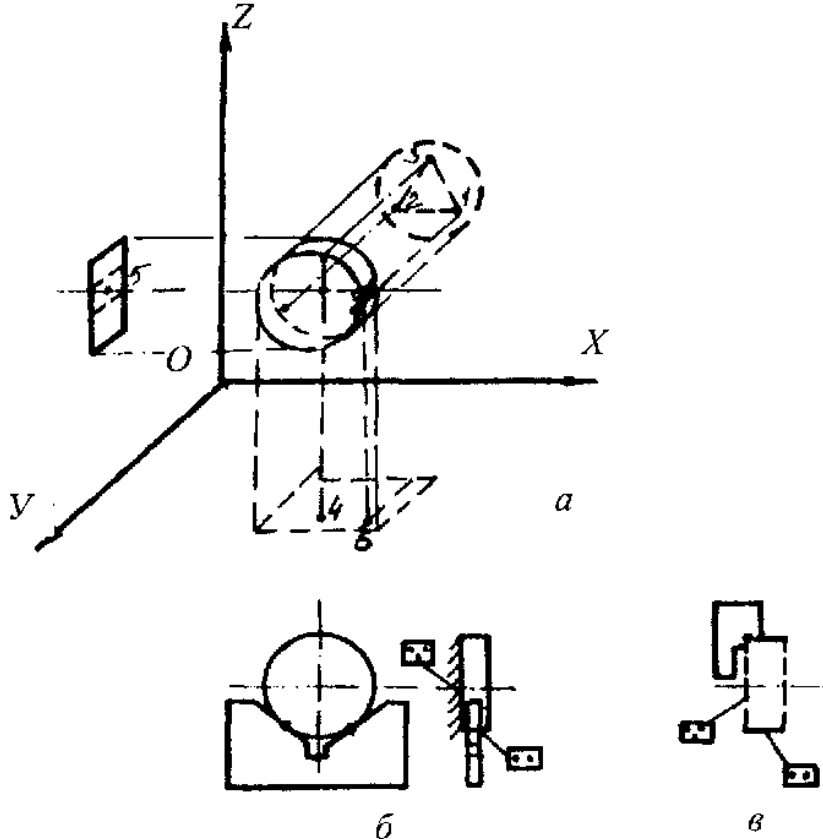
Схеми базування коротких циліндричних заготовок
